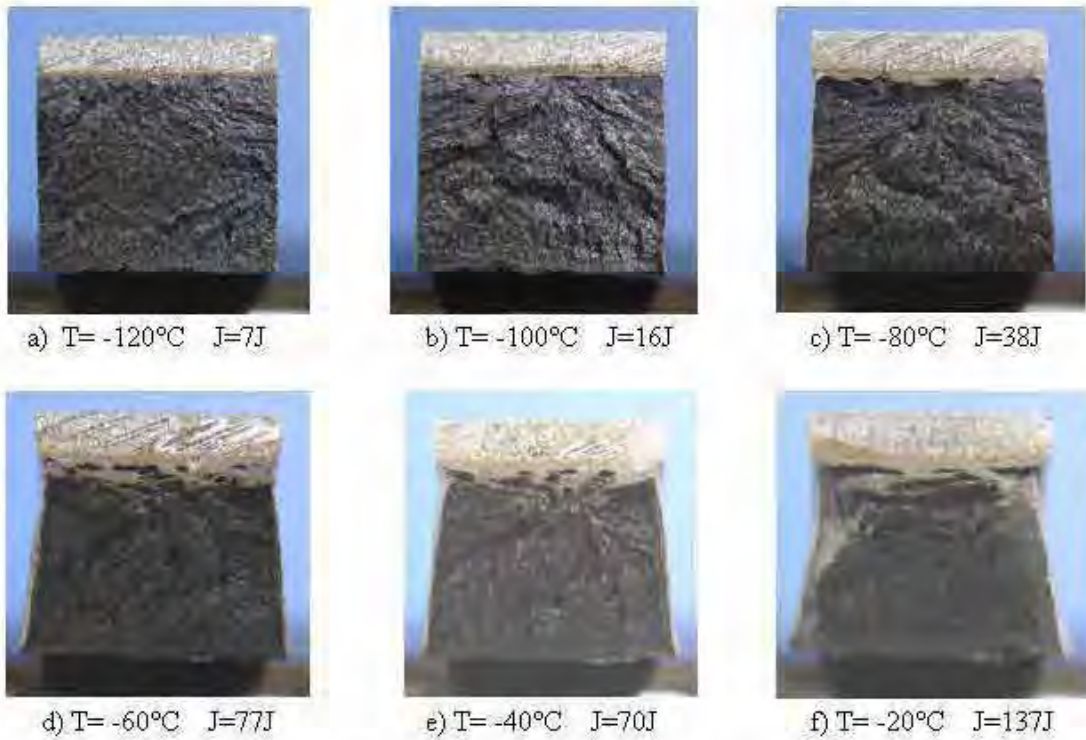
Fractografia da superfície de fratura do aço A516 - CF, corpo-de-prova entalhado.
